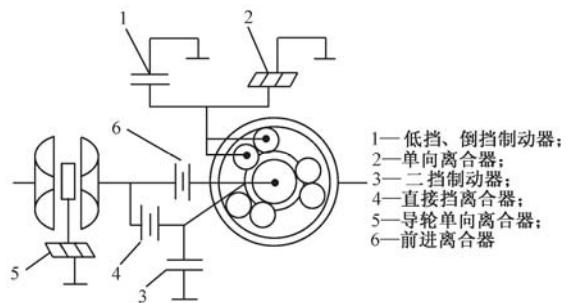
3 挡拉维娜式行星齿轮变速器结构简图
